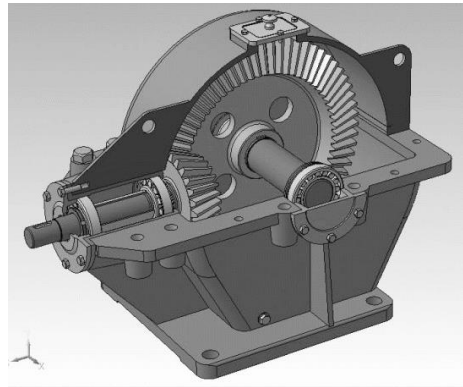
Конічний одноступінчастий редуктор без кришки
